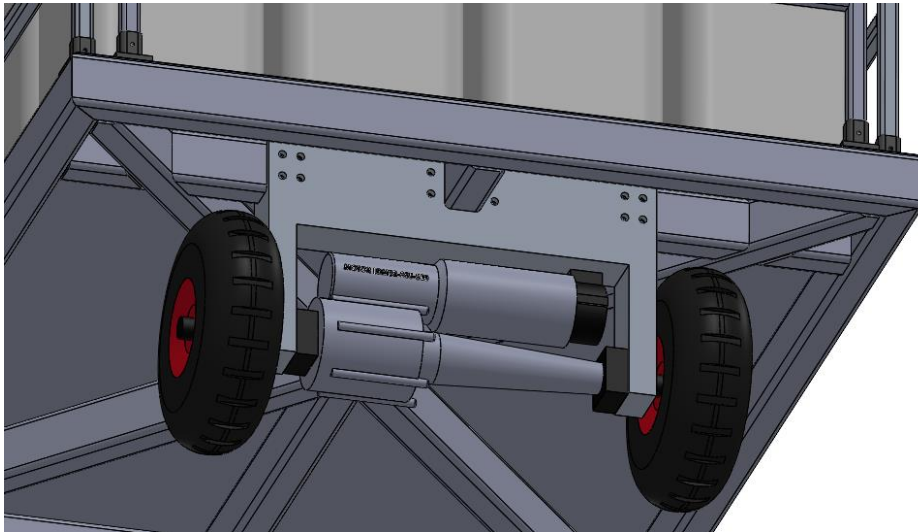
Modelo CAD unión CHASIS – MOTOR [fuente propia]
